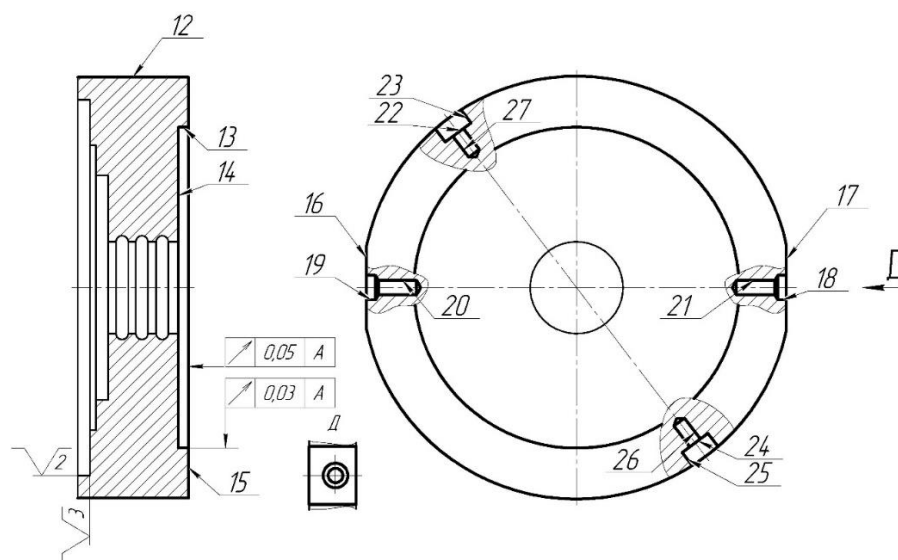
Эскиз для получения ступенчатых отверстий
